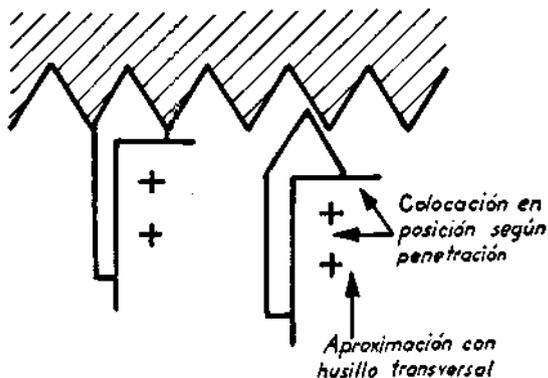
Colocación de la herramienta sobre la rosca exterior
